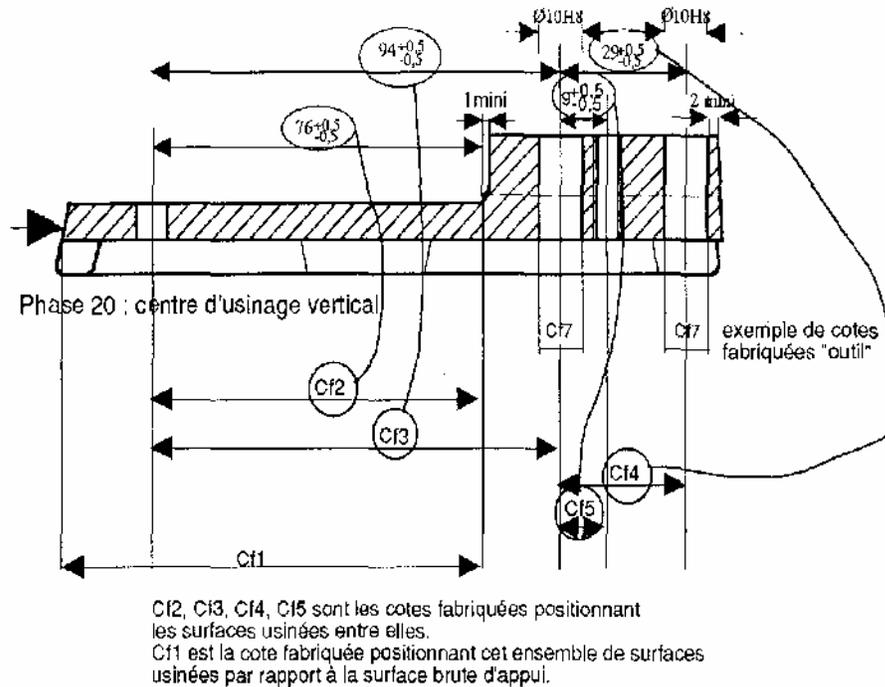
Choix des cotes fabriquées définissant les usinages.
